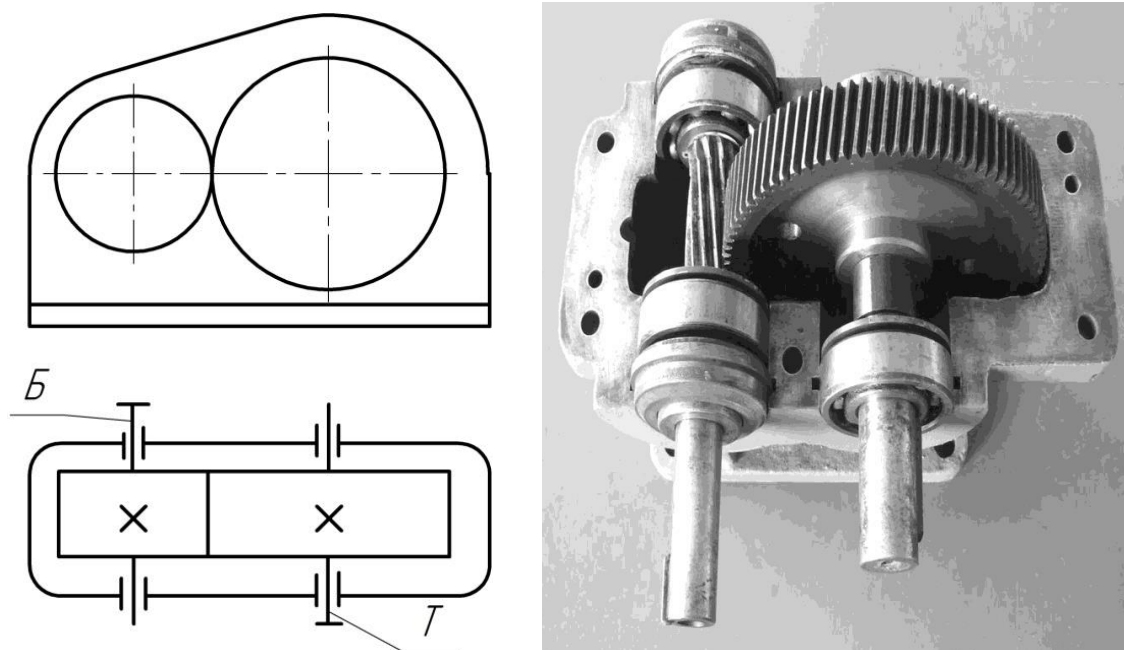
Одноступенчатый горизонтальный редуктор
